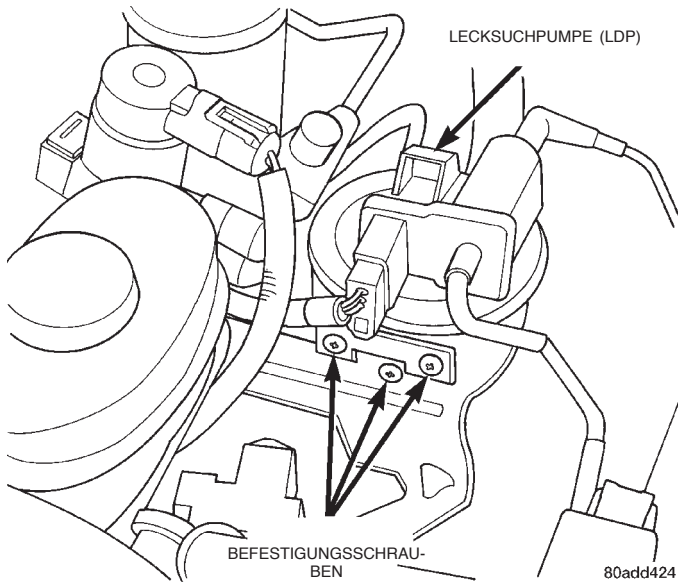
Befestigungsschrauben/Lecksuchpumpe (LDP)
